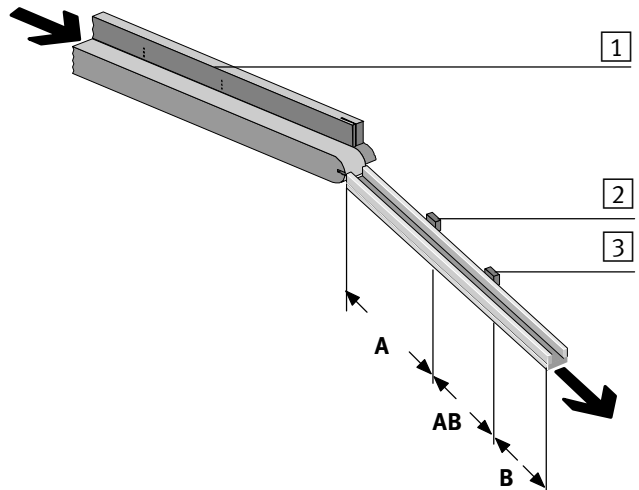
/3: Staustrecken-Kontrolle mit Hysterese
